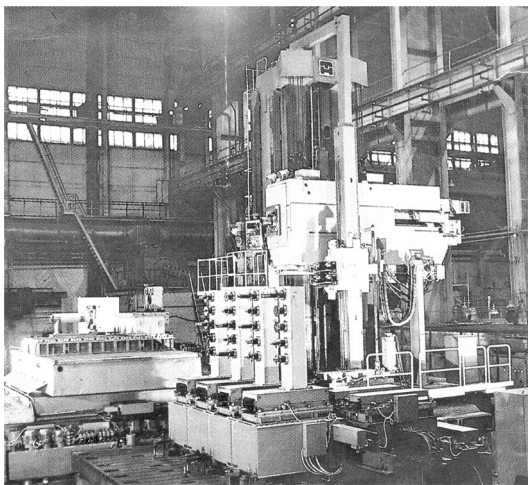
Тяжелый многоцелевой станок сверлильно-фрезерно-расточной группы с поворотно-подвижным столом для обработки корпусных деталей массой до 200 т
